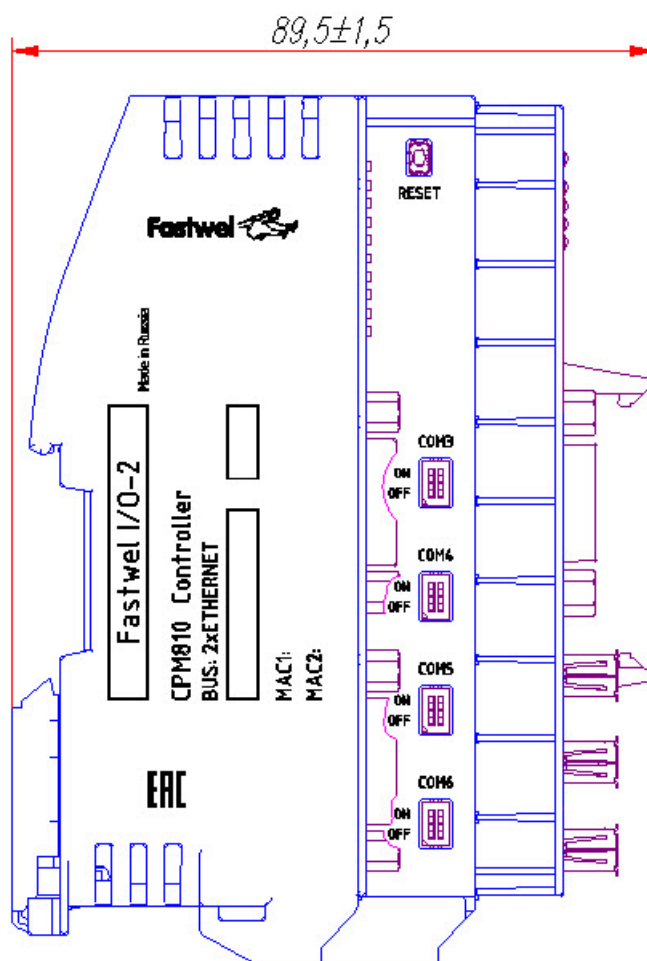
Расположение элементов изделия на боковой панели и габаритные размеры с установленными разъемами
